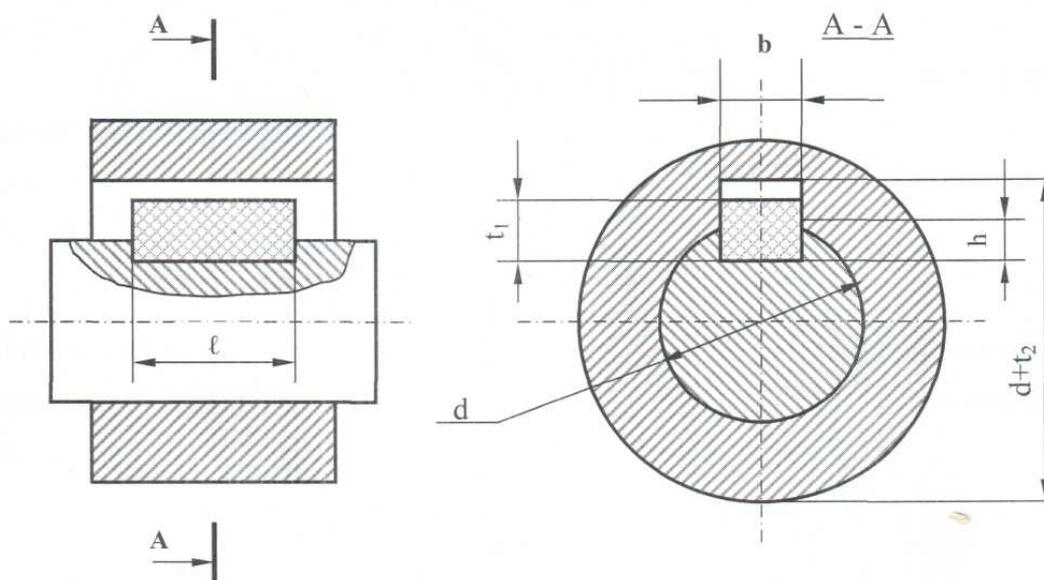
Размеры шпоночного соединения с призматической шпонкой
